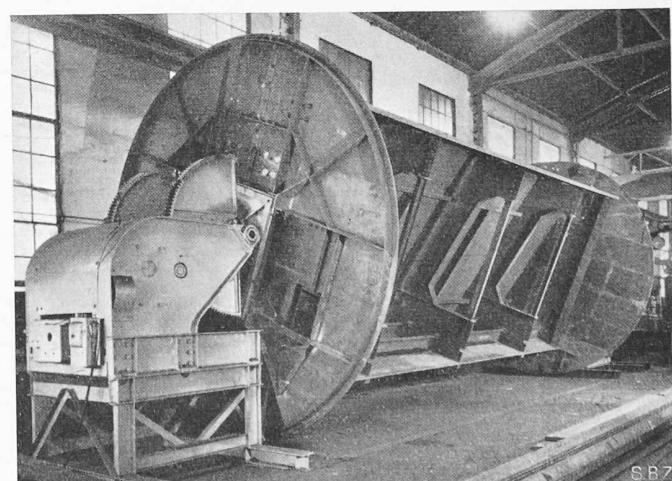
Drehvorrichtung für die Schweissarbeiten mit Teilen des untern Kastenträgers
